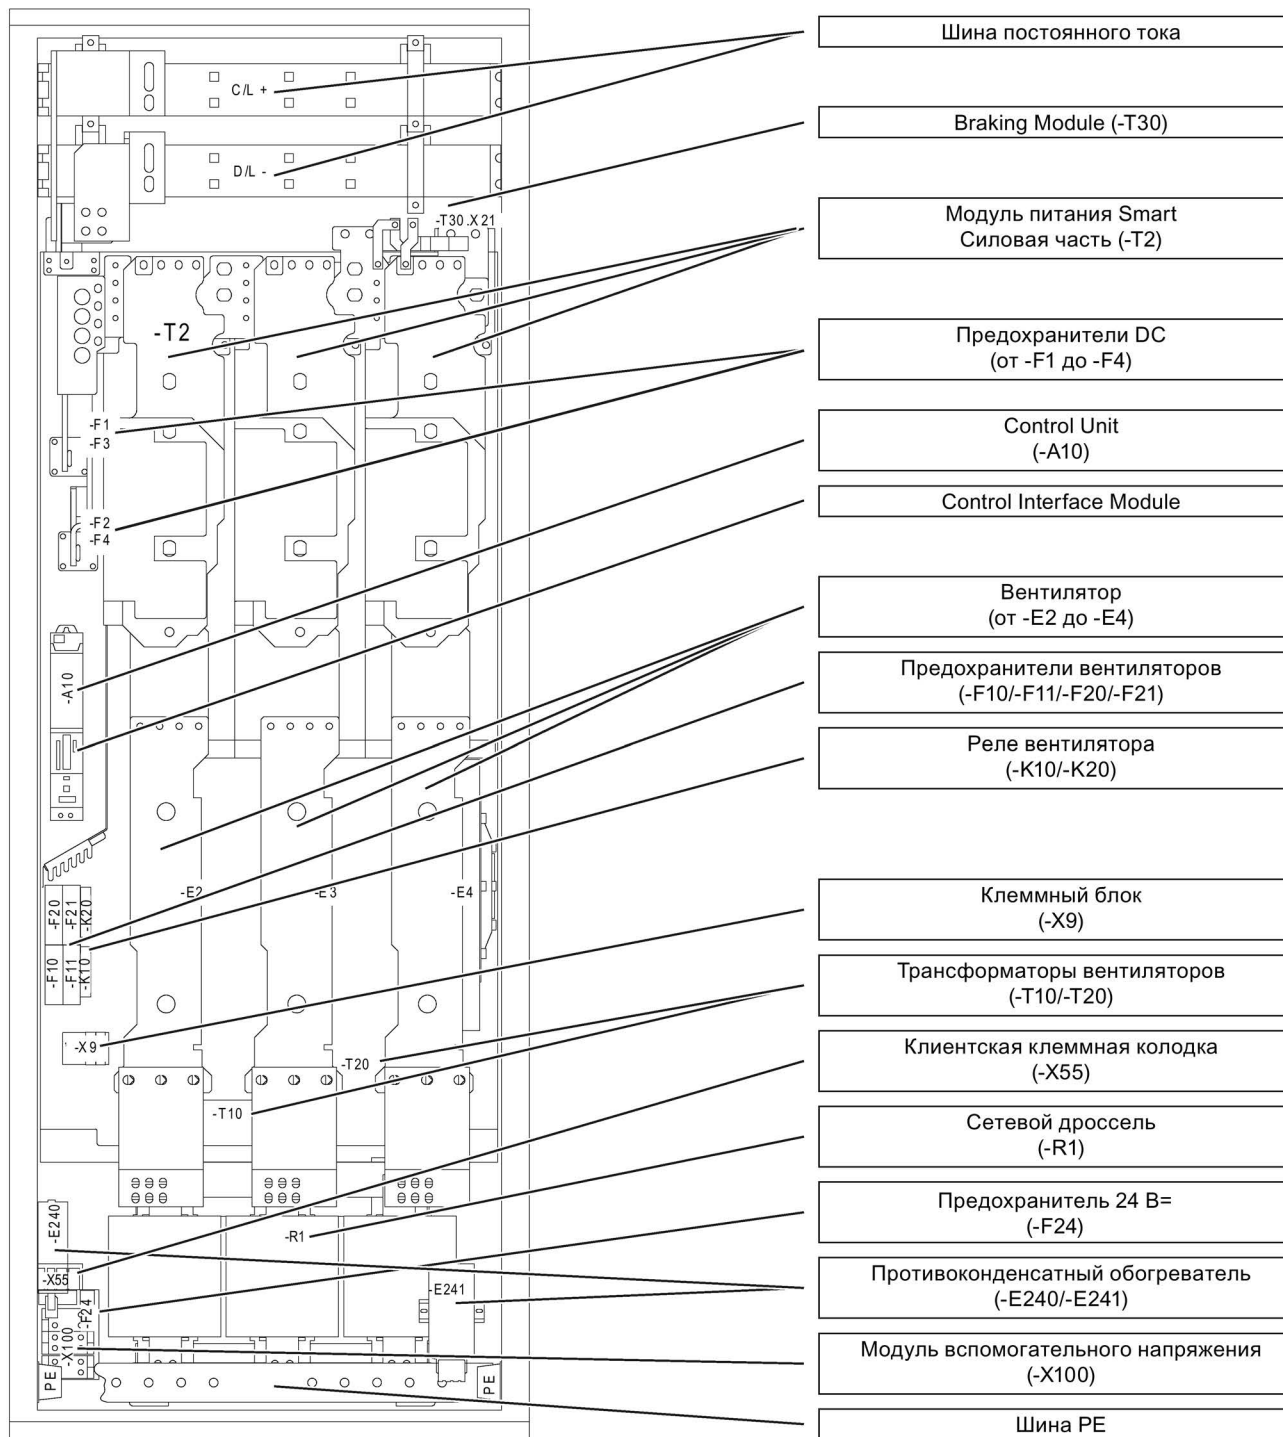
Пример сборки модуля питания Smart (типоразмер JX)
